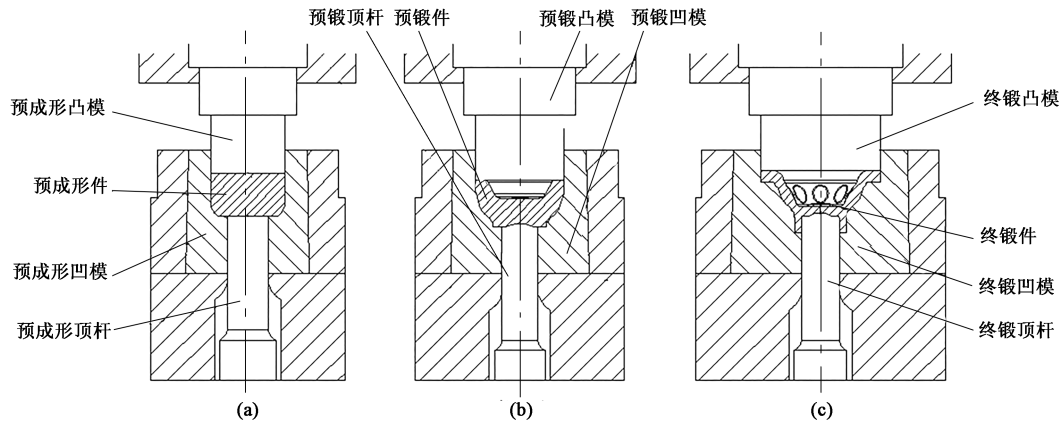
法兰盘零件 3 工位热模锻模具结构示意图
